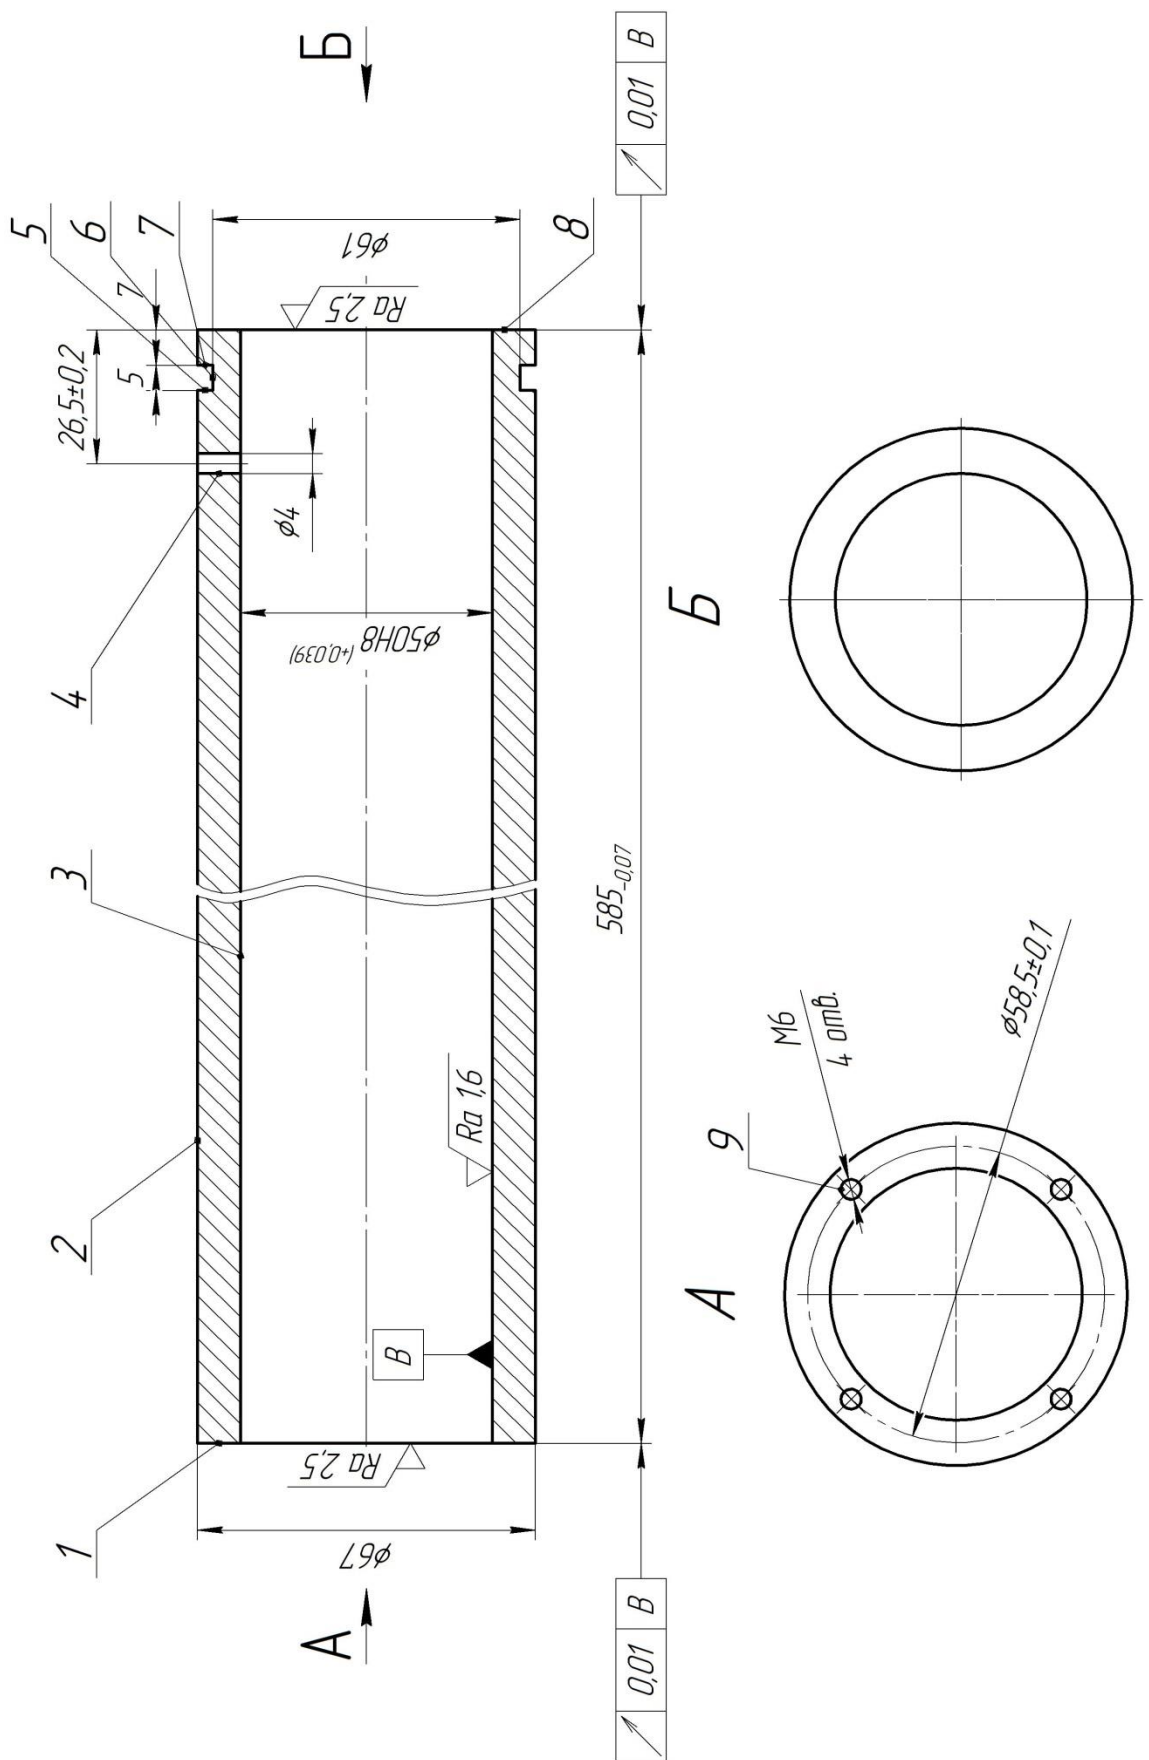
Общий вид детали - «Корпус гидроцилиндра»
